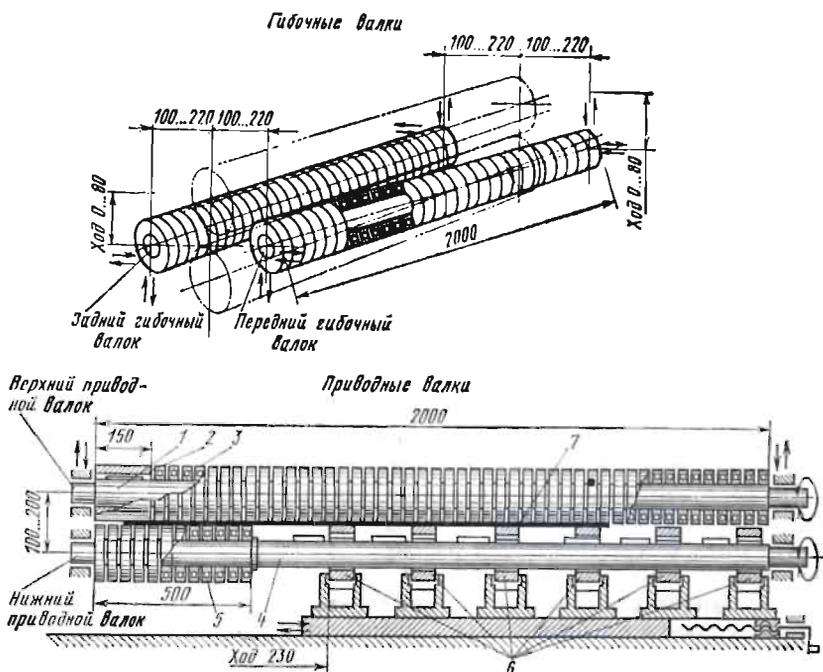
Валки гибочного листового станка ГЛС-2К
